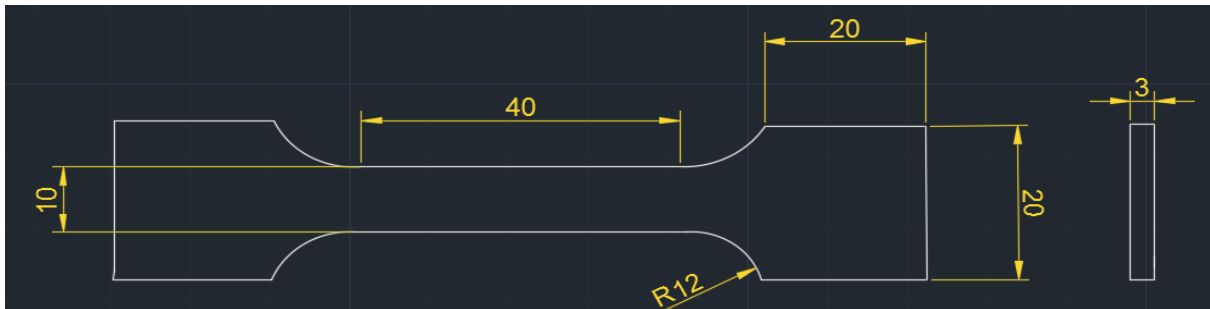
Desenho técnico dos provetes para os ensaios de tração.
